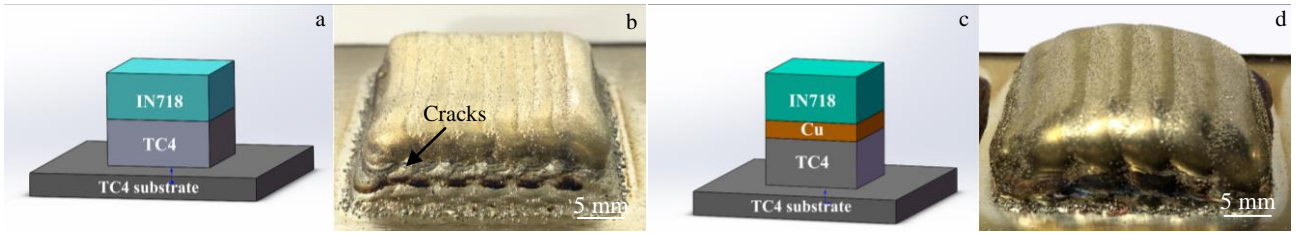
TC4/IN718 双金属结构示意图与样件宏观形貌
